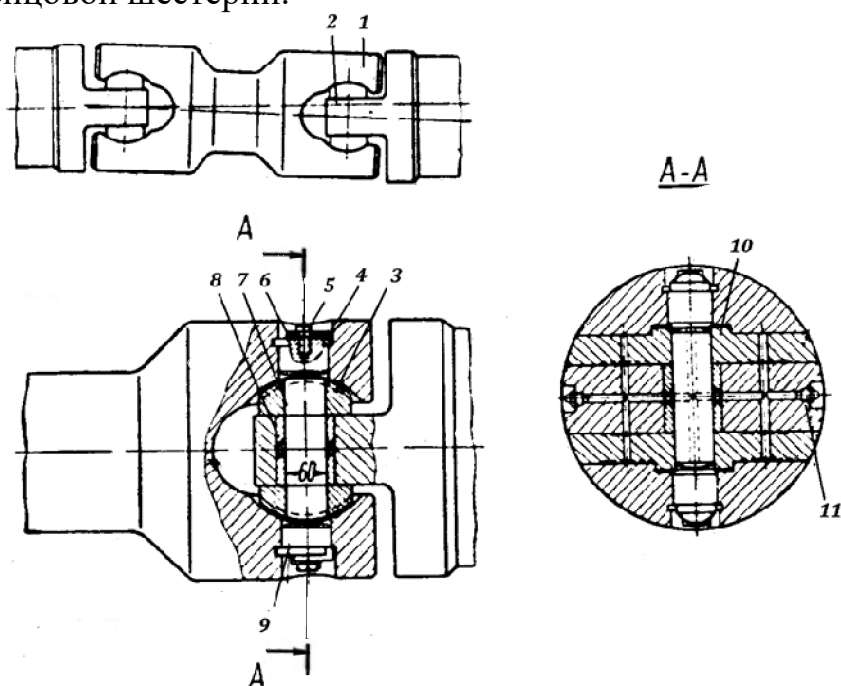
Схема универсального шпинделя привода крупногабаритных барабанных аппаратов:
